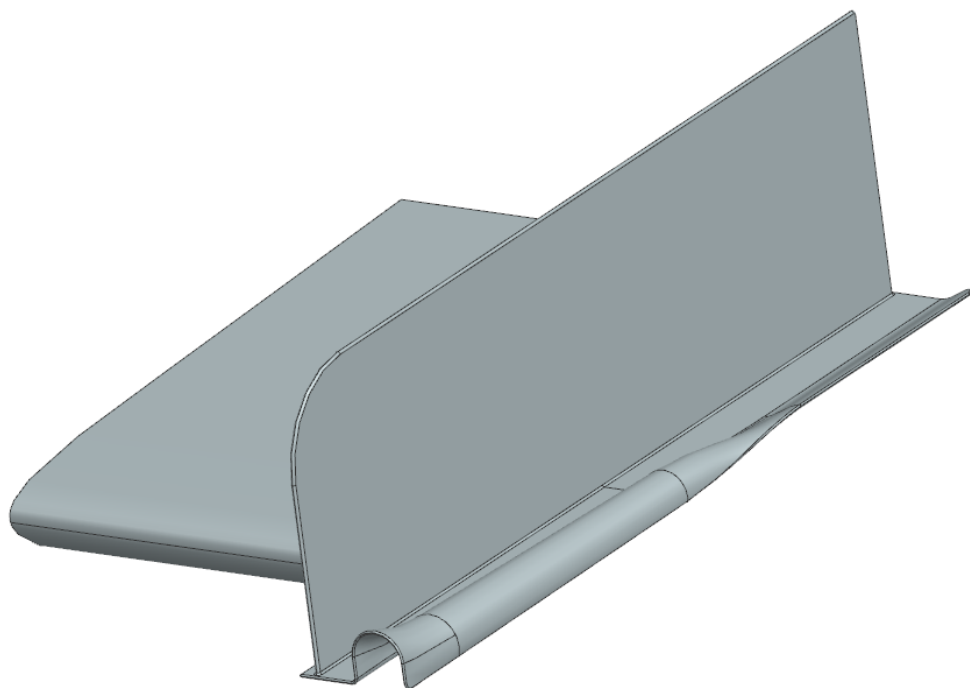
Vista prospettica dell'ENDPLATE 3
